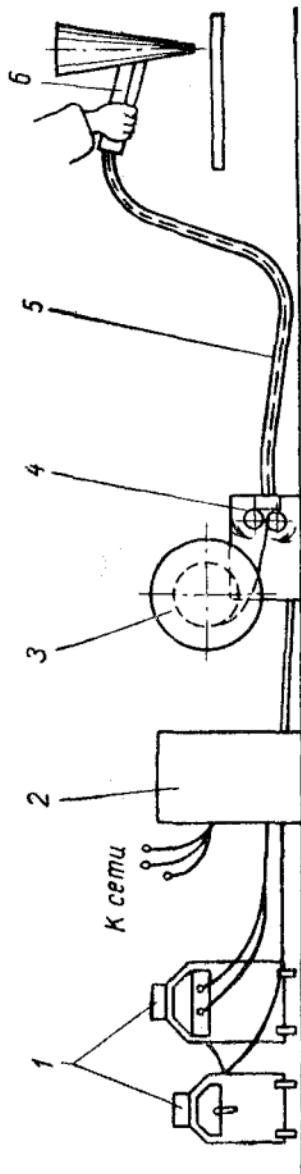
Схема сварки шлангом полуавтоматом ПШ-5
